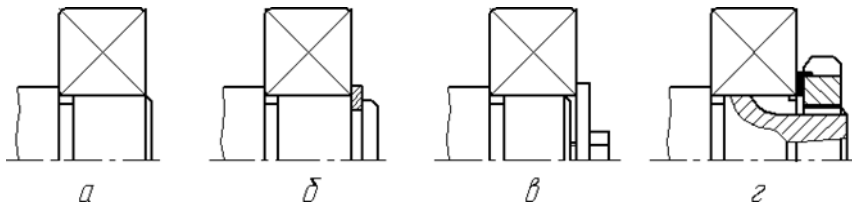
Монтаж підшипників кочення на валах.
